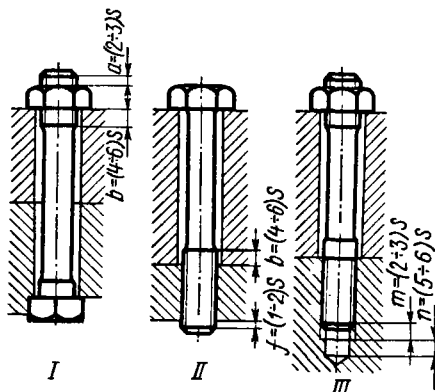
Размеры свободных участков резьбы для основных крепежных соединений
